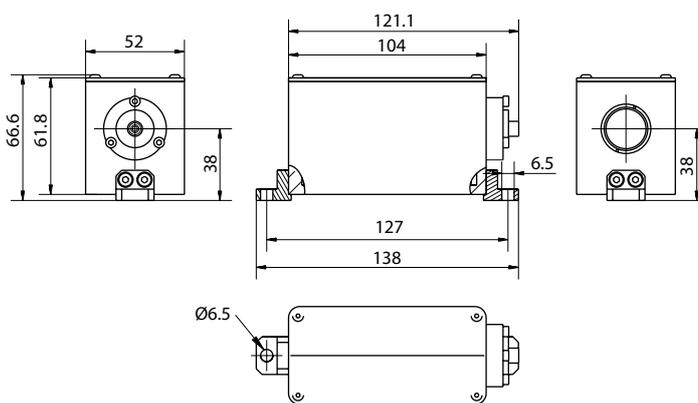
Габаритные размеры коллиматора с изолятором лазера модели FPS200.
